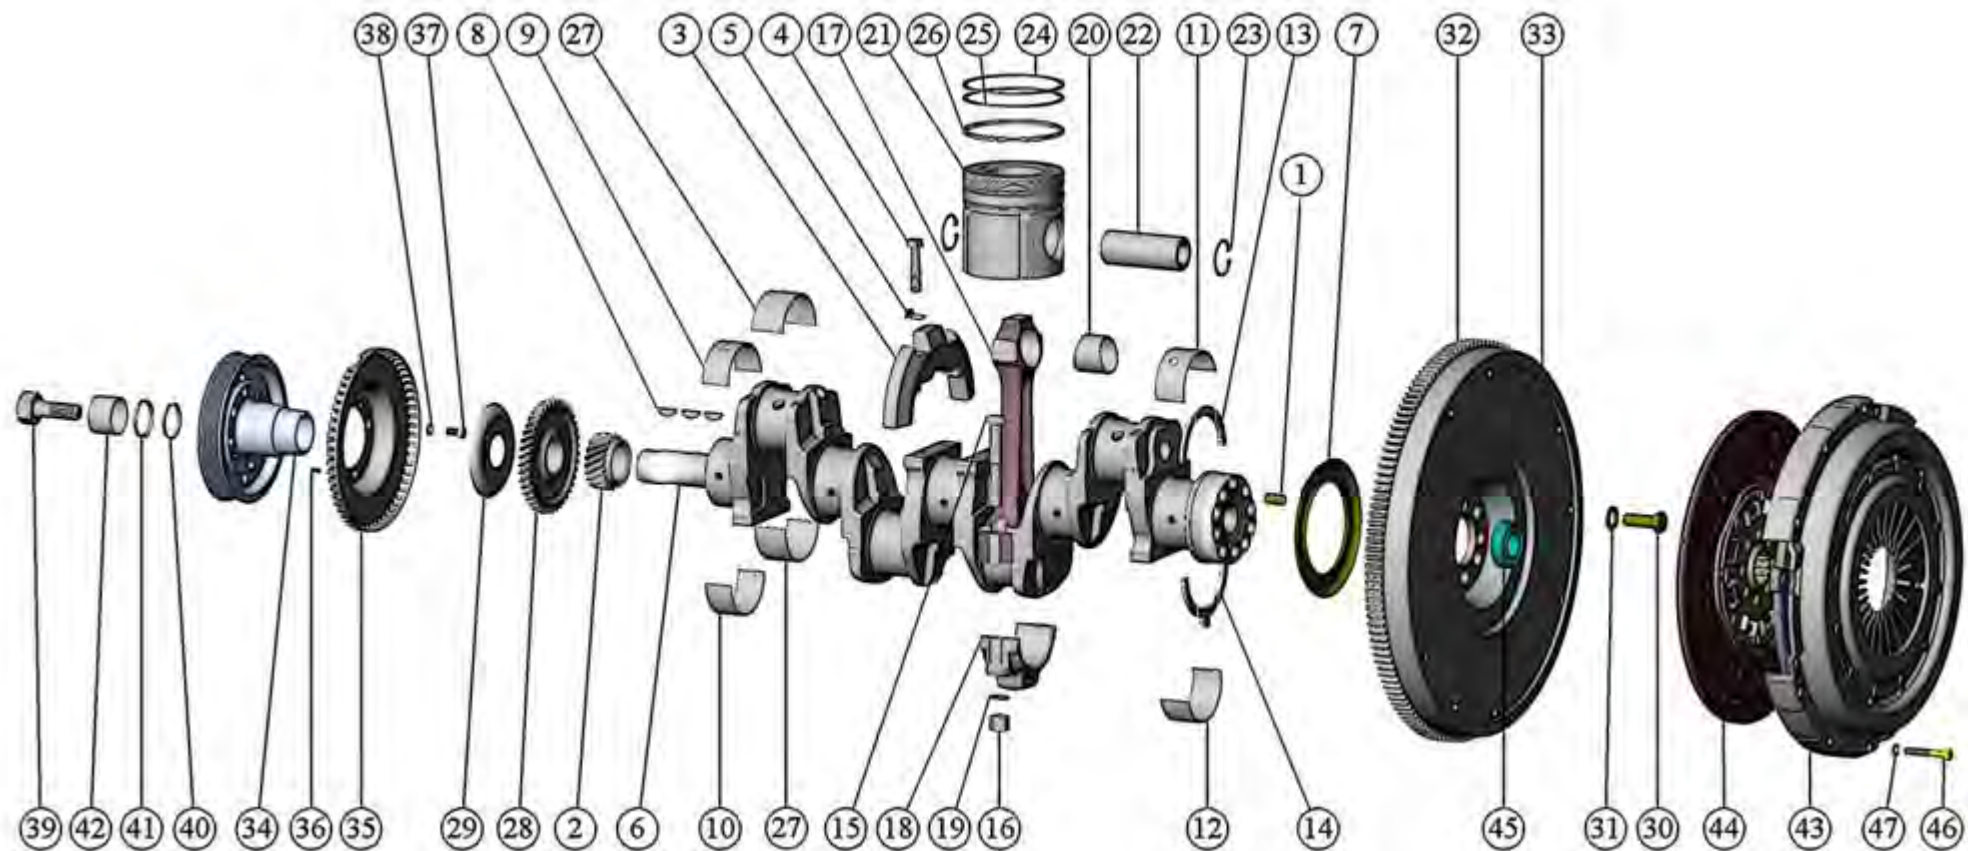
Кривошипно-шатунный механизм. Установка шкива коленчатого вала. Установка муфты сцепления.
